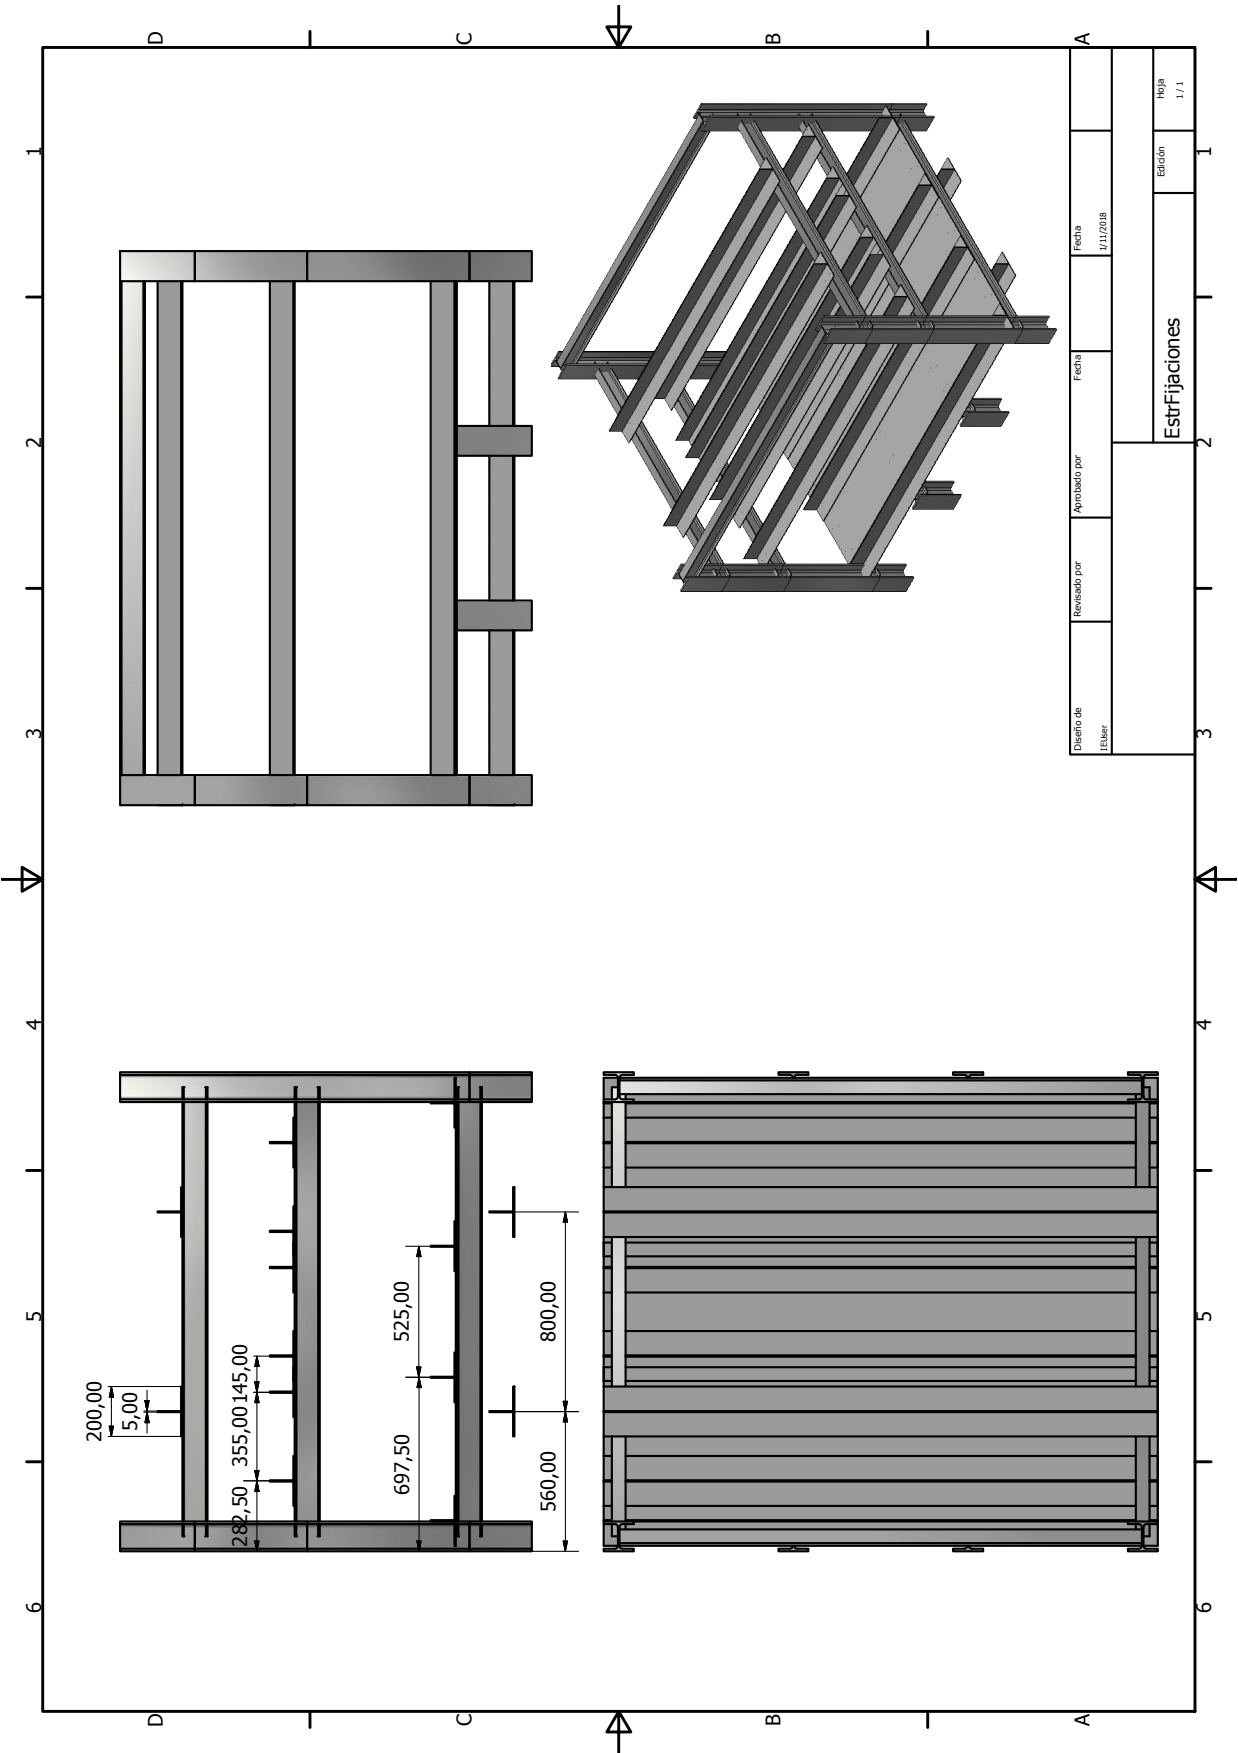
Estructura de soporte con los elementos de fijación (mm).
